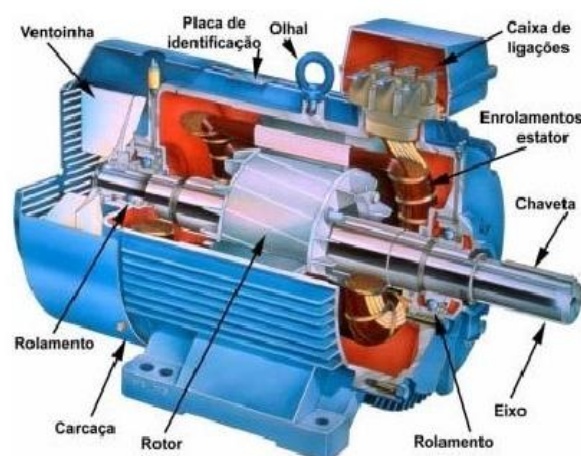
Os componentes que constituem um motor elétrico. [17]
